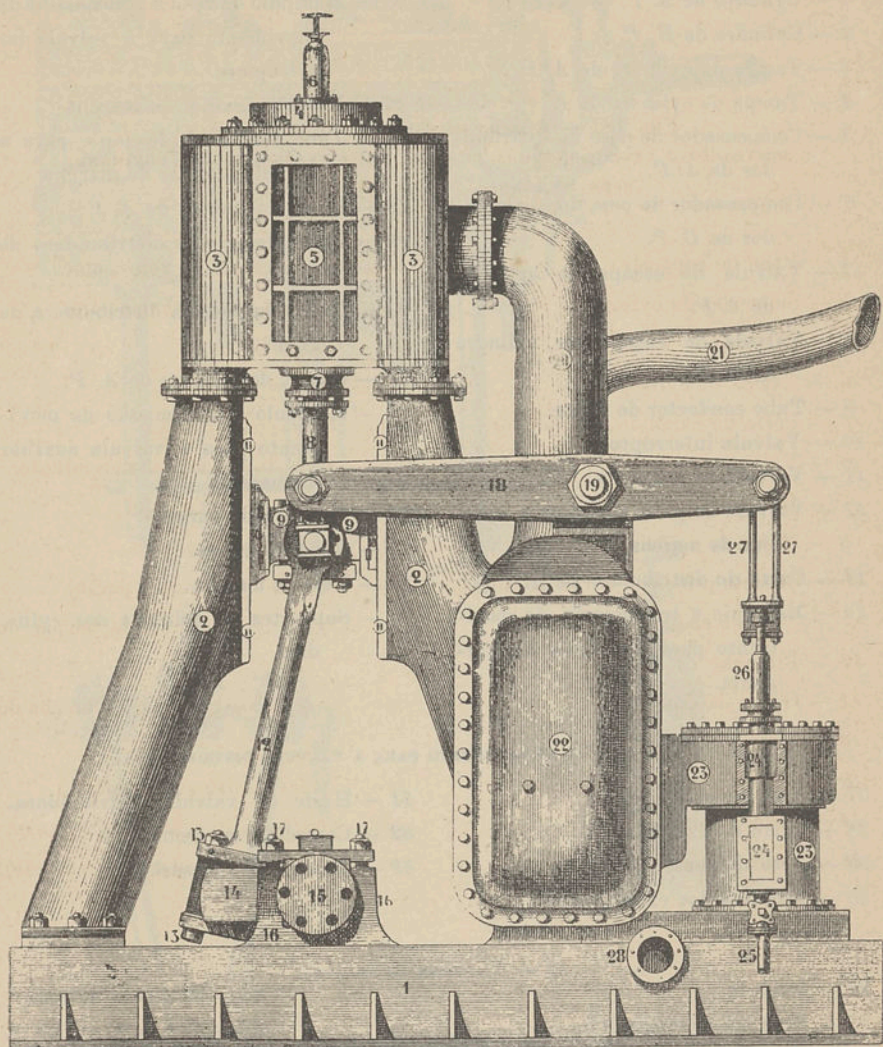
ALÇADO TRANSVERSAL DE UMA MACHINA,
